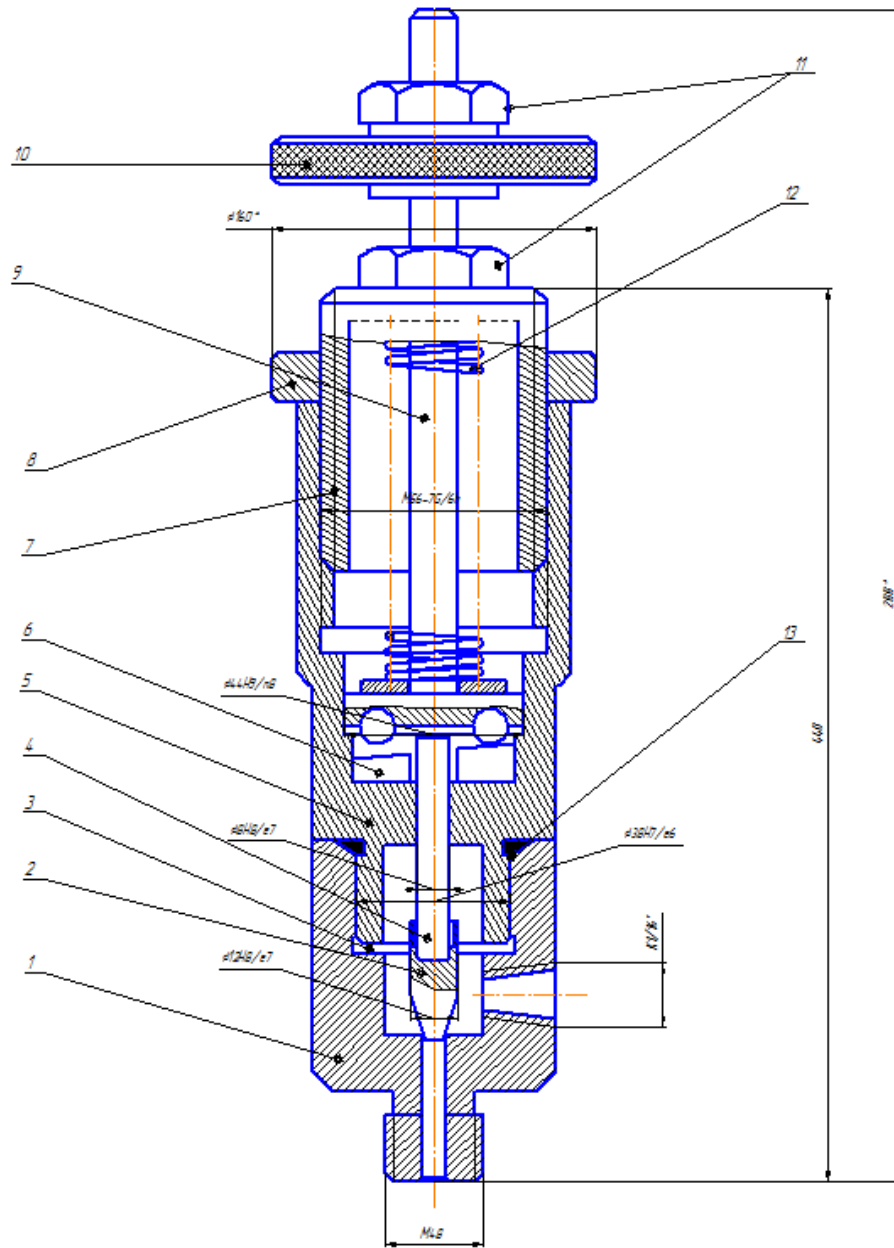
Принципиальная схема приспособления для заправки
